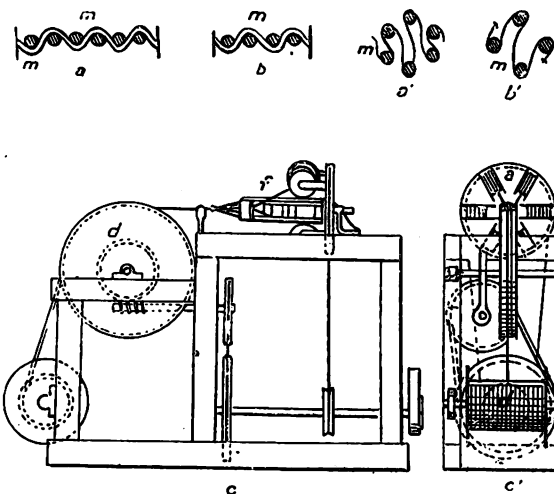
Machine à fabriquer les câbles téléphoniques.
